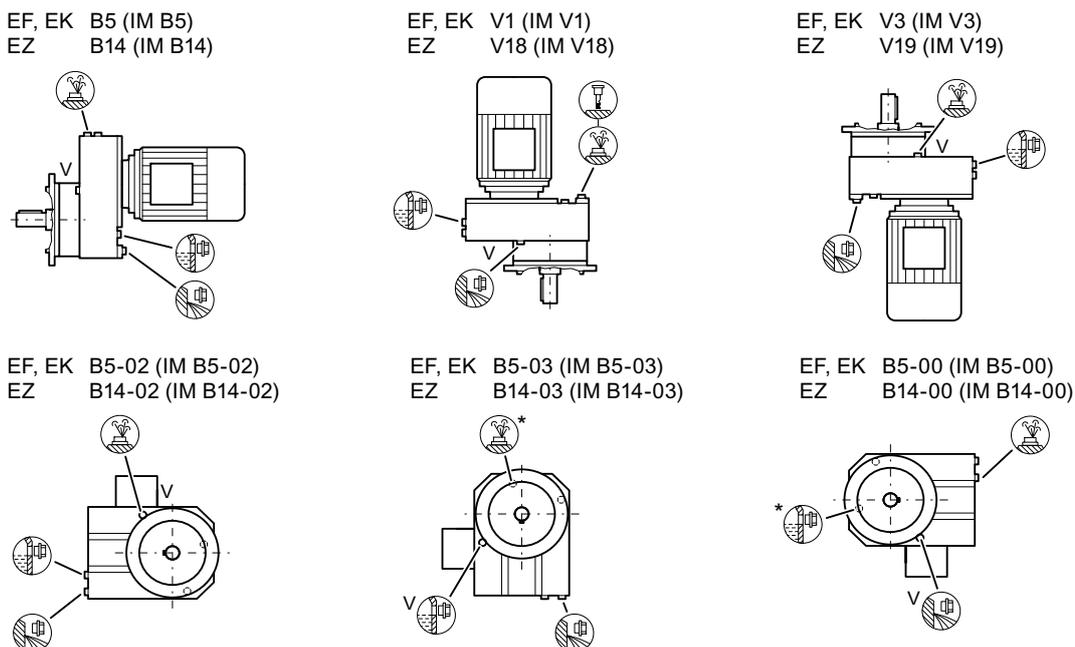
Formes de construction pour E, tailles 38 - 148
